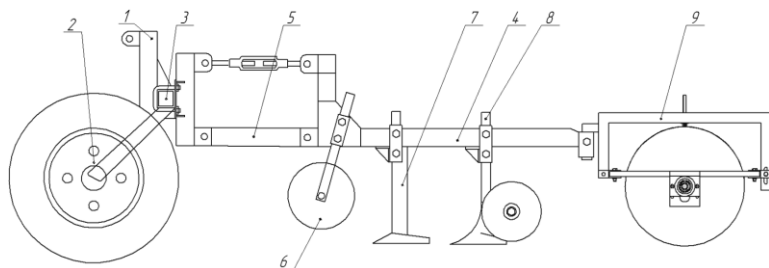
Схема гребневой сеялки-культиватора: 1 — сеялка; 2 — приводное колесо; 3 — рама; 4 — секция; 5 — параллелограммный механизм; 6 — копирующее колесо; 7 — сошник двухуровневого высева семян и удобрений; 8 — орудники; 9 — каток-гребнеобразователь
